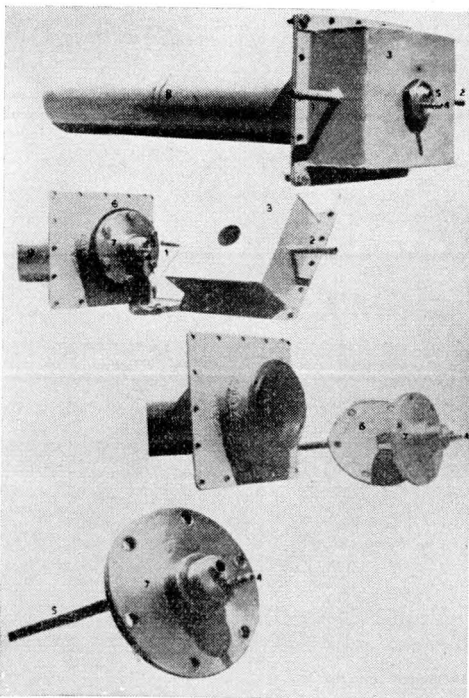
Fotos da caixa em detalhes. 1 — Entrada de água de refrigeração do flange. 2 — Saida da água de refrigeração do flange. 3 — Caixa de refrigeração. 4 — Tomada de ligação do vácuo. 5 — Gacheta de borracha. 7 — Flange de vedação da caixa. 8 — Corpo da caixa.
